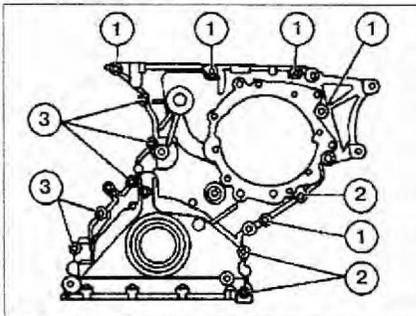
Порядок затяжки болтов крепления крышки цепи ГРМ.
